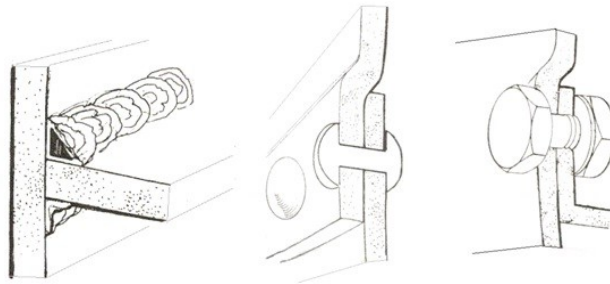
Uniones más comunes. Soldadura, Remachado, Atornillado.
